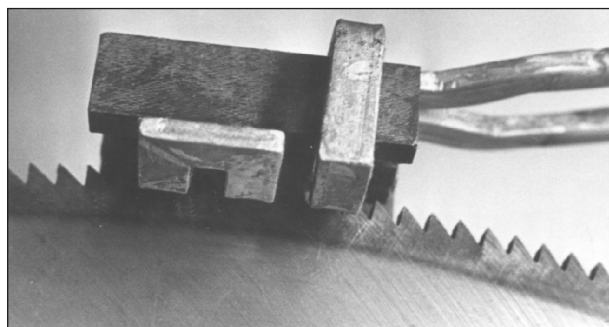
Общий вид индуктора и расположение в процессе закалки относительно пилы
